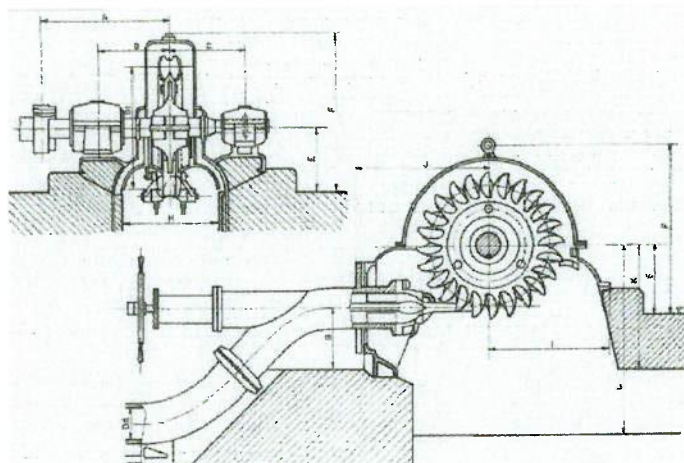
Turbina Pelton de 1 Jato de Eixo Horizontal.
